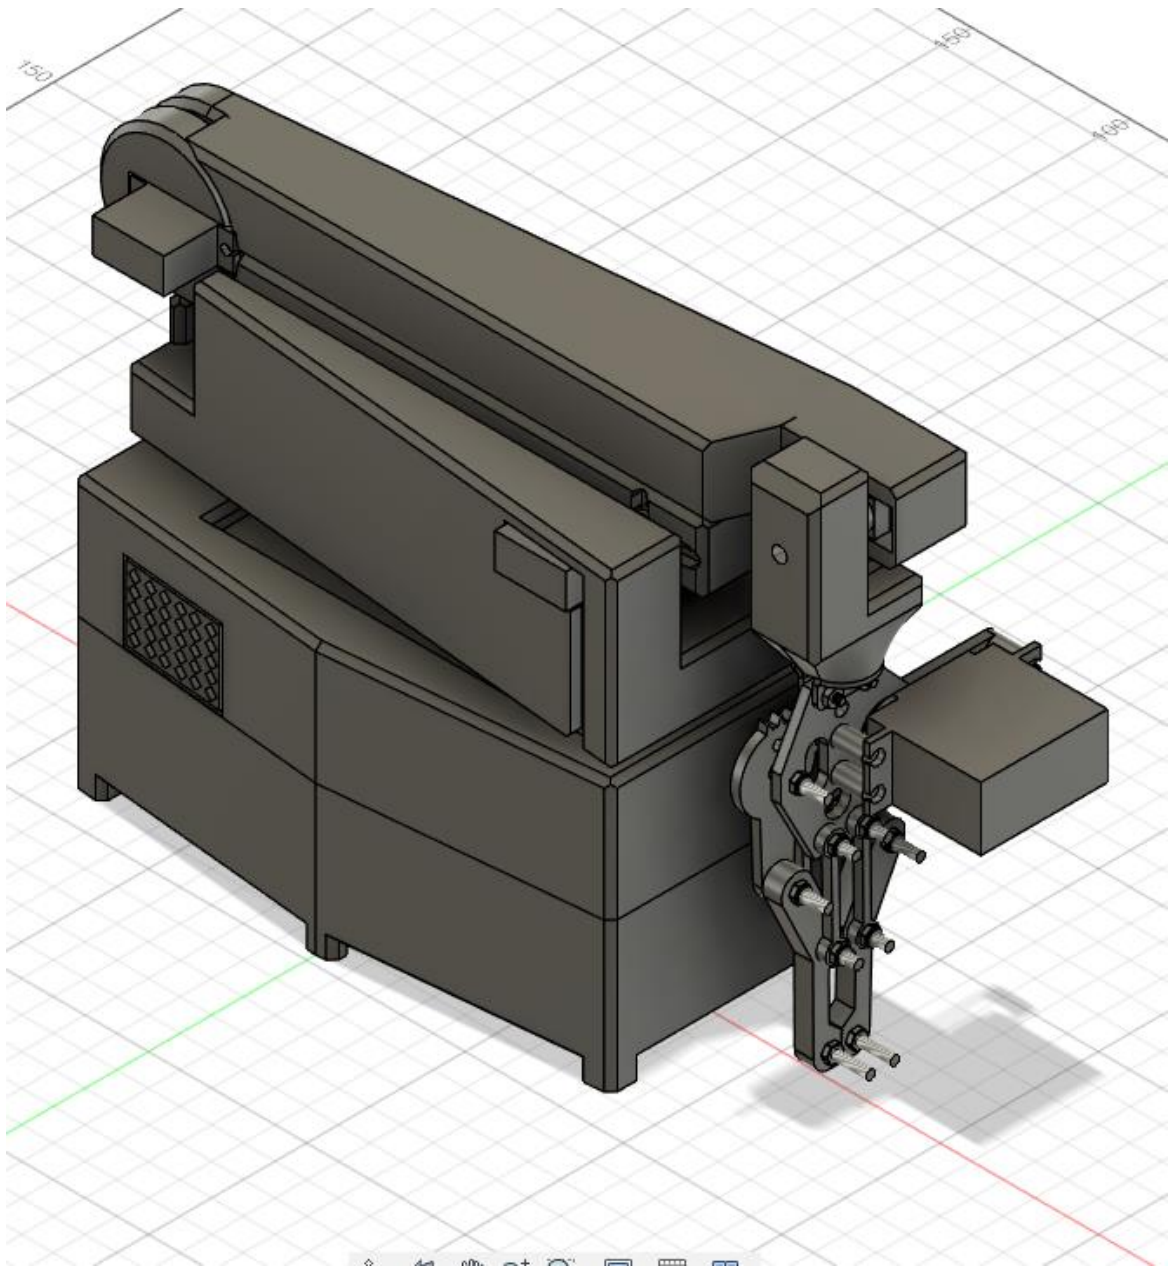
Ізометричний вид на корпус маніпулятора в стані «сну» (Вид 1)
